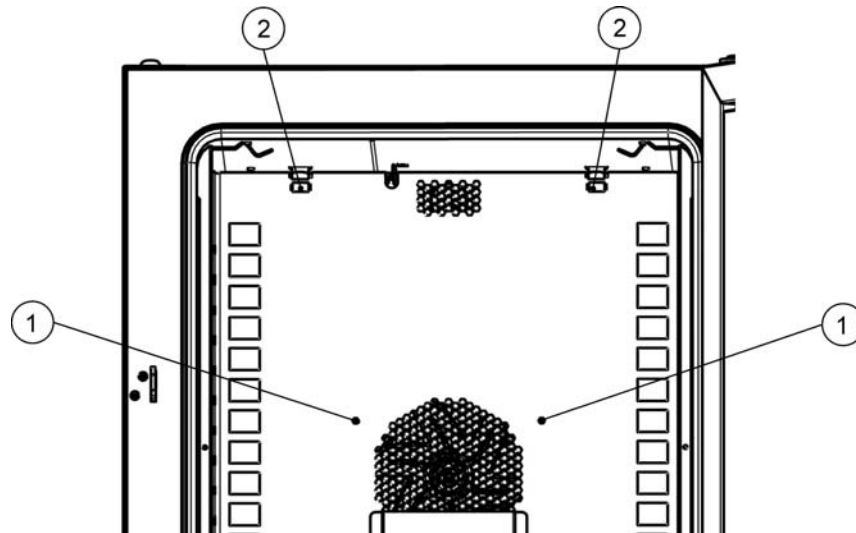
Installation du déflecteur d'air de la paroi arrière
